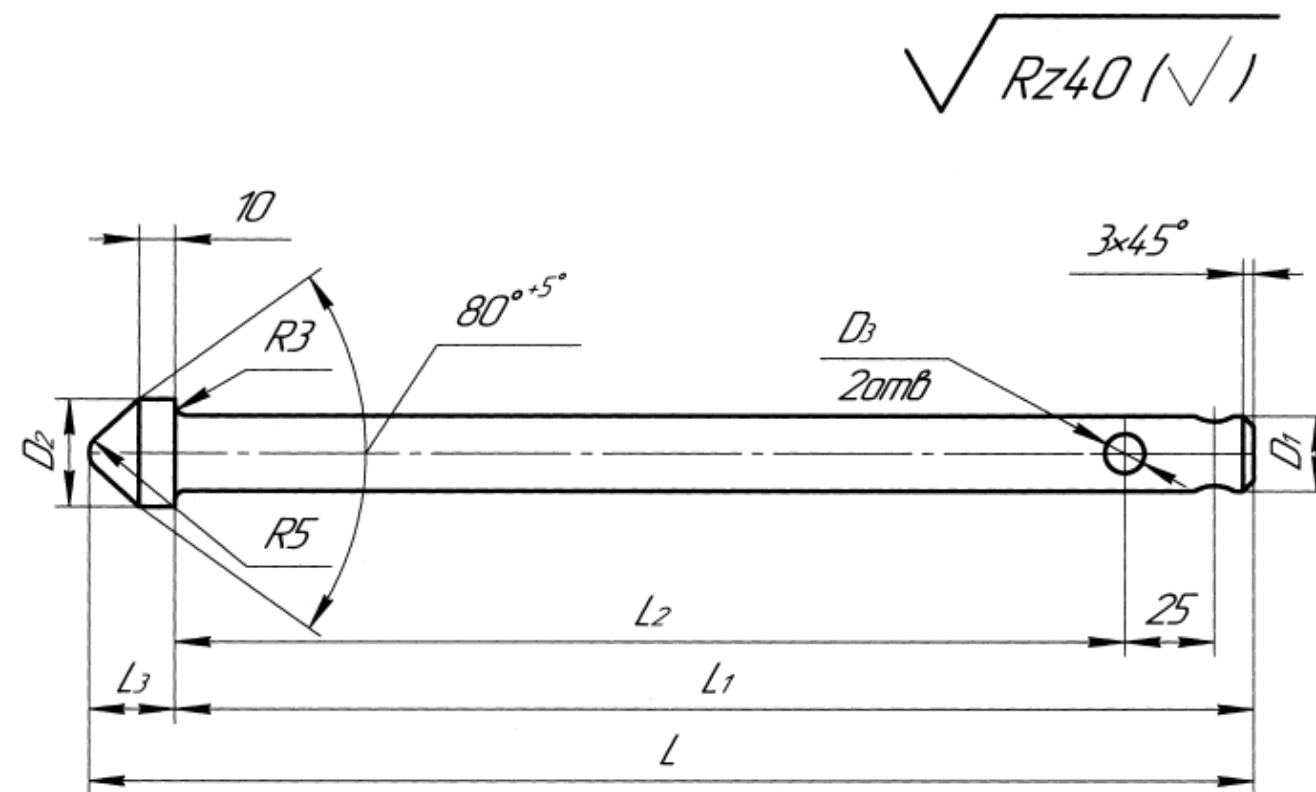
Чертеж оправки автоматического стана ТПА 220
